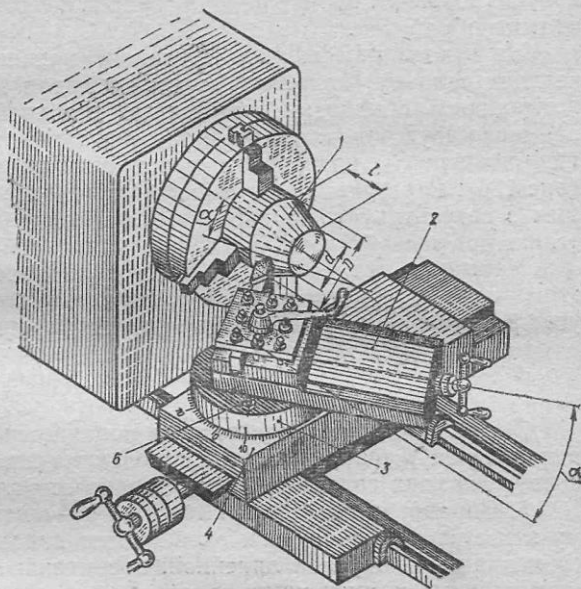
Обработка конуса при повернутых верхних салазках суппорта.
